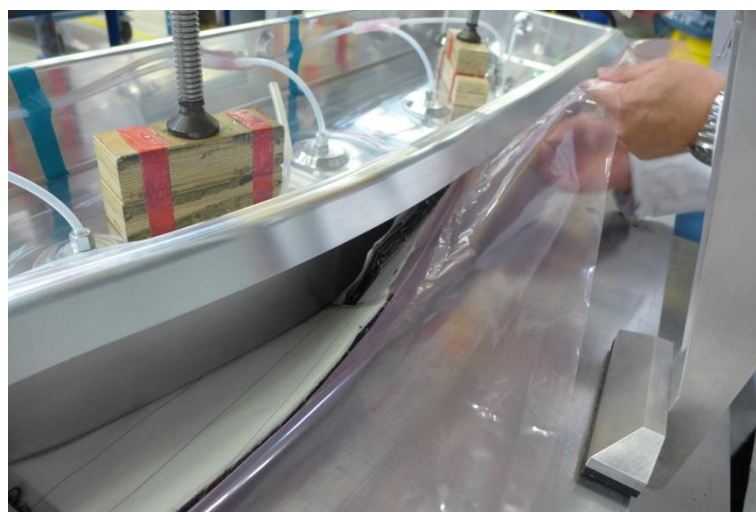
Manuelles Fixieren der Preform auf dem Werkzeug
